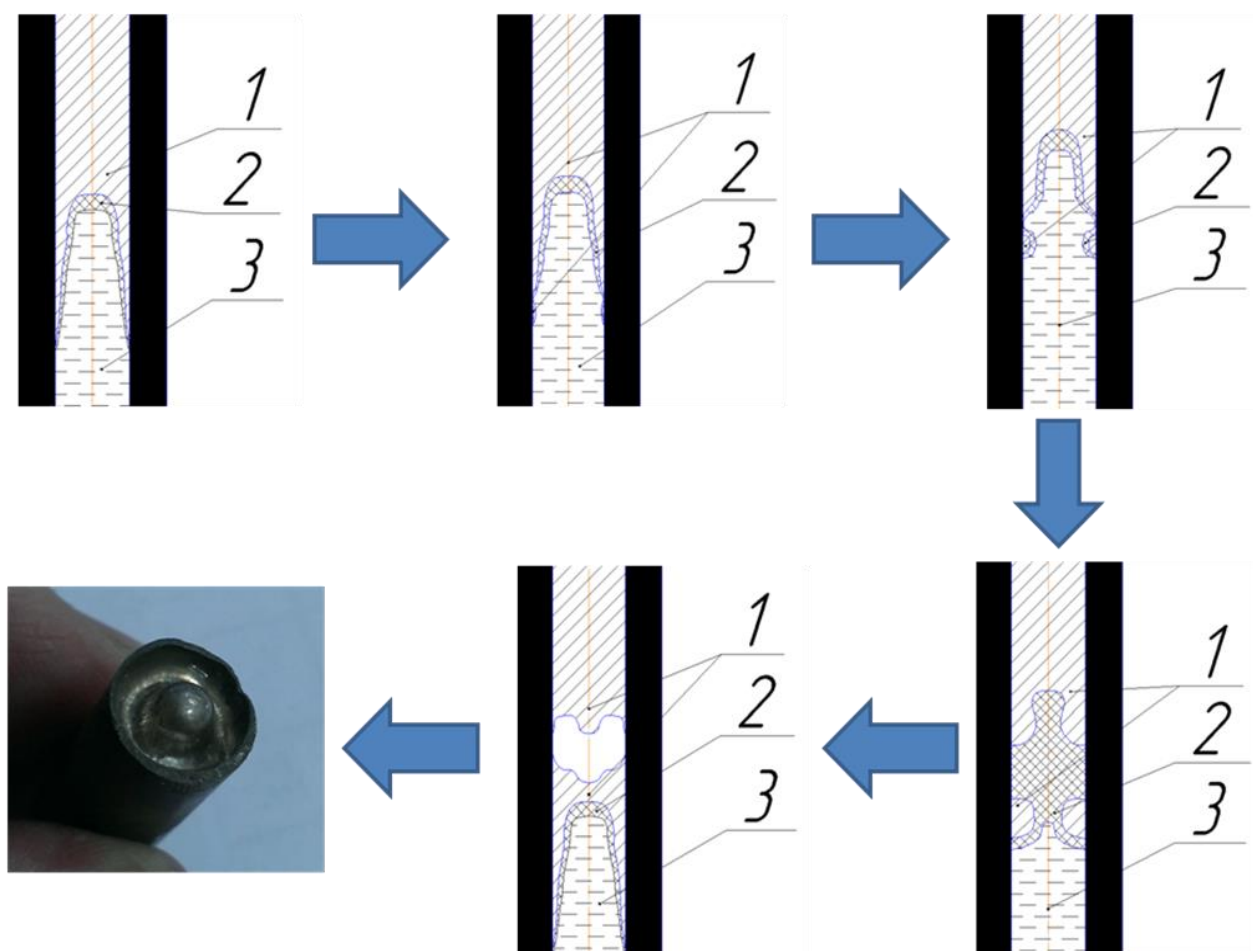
Схема образования обрыва заготовки: 1 – сформировавшаяся заготовка; 2 – двухфазная область; 3 – расплав.
